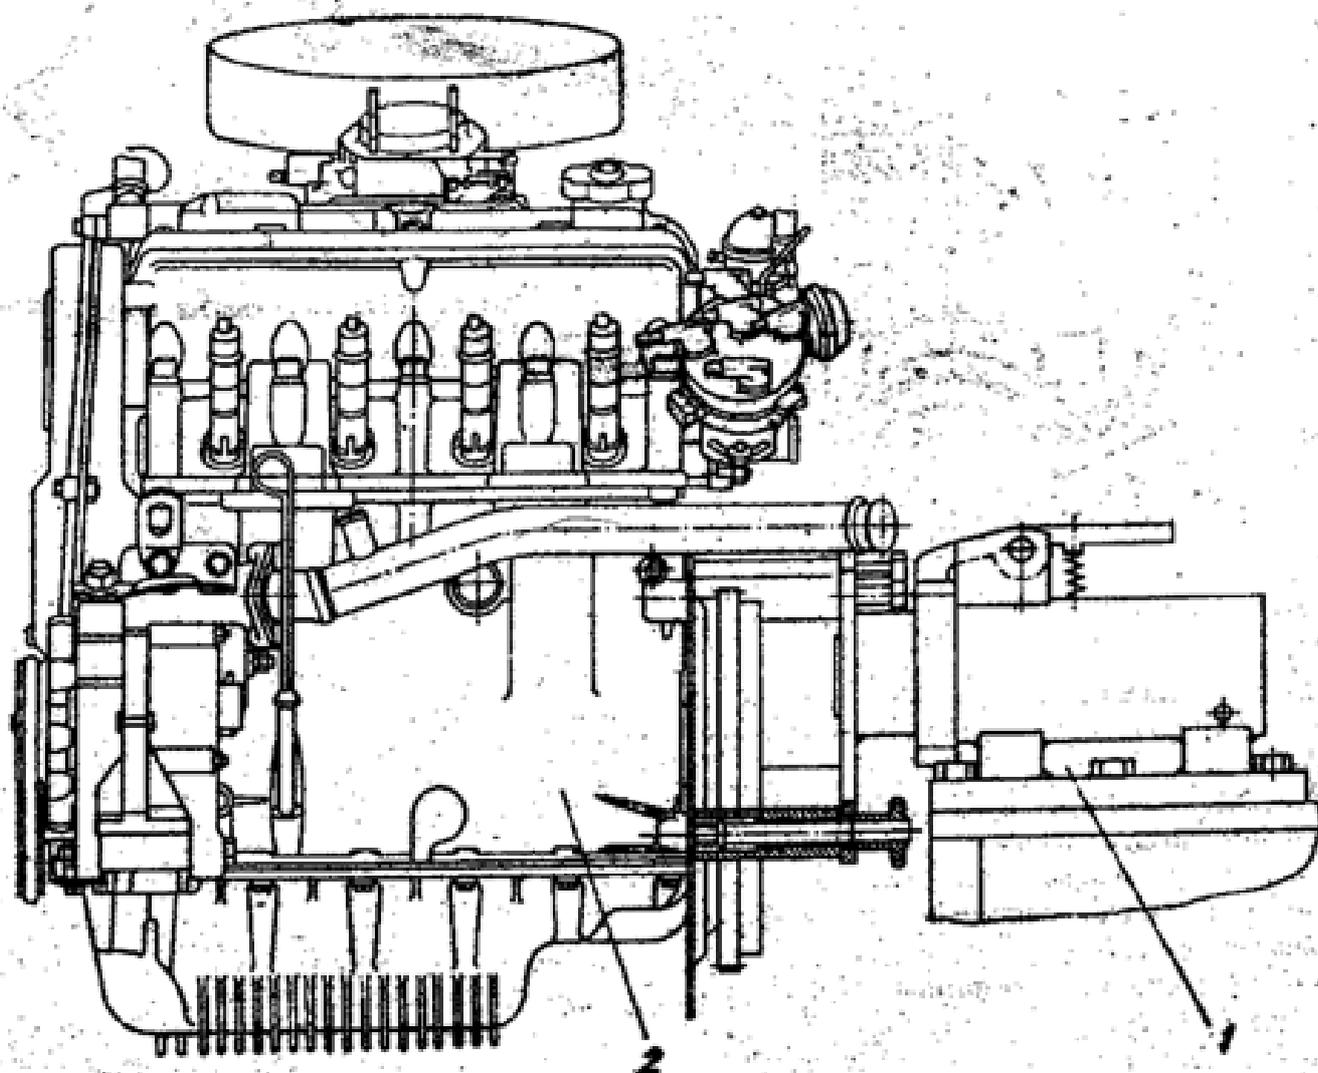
Двигатель, установленный на приспособление для разборки и сборки: 1-приспособление для разборки и сборки М9832-345; 2-рукоятка
